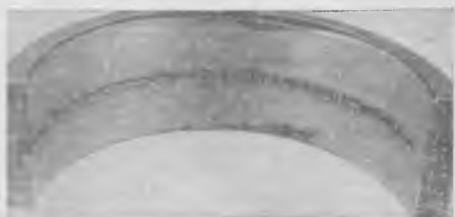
Разрушение трущейся поверхности алюминиевого коренного вкладыша при нарушении условий смазки
